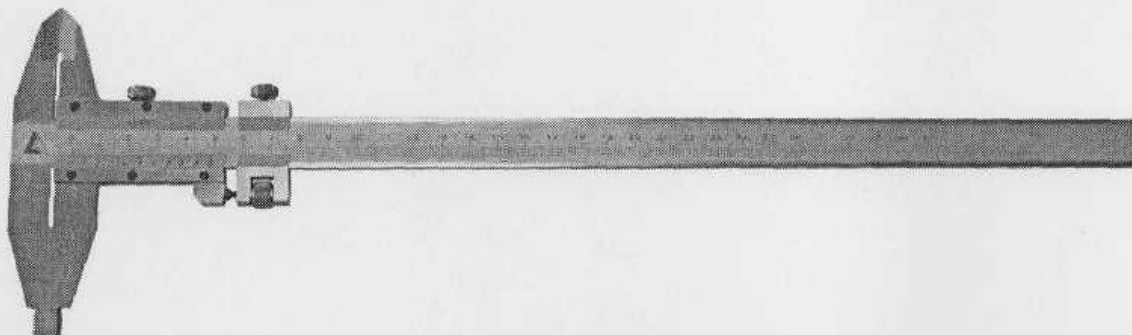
Внешний вид штангенциркулей ШЦ-II
